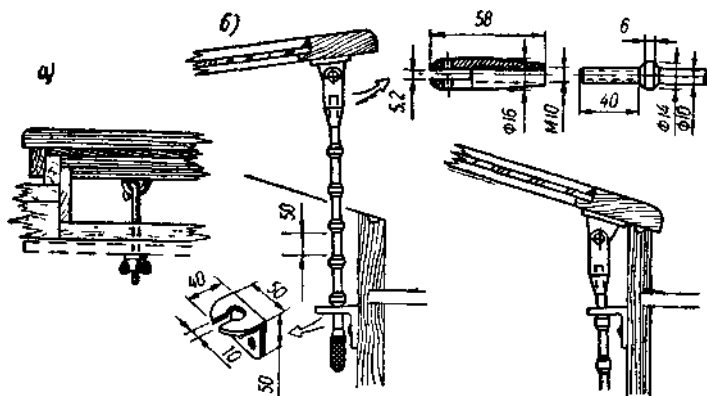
Задрайки люков: а — задрайка с винтом на барашках; б — задрайка с фиксированным положением крышки люка
